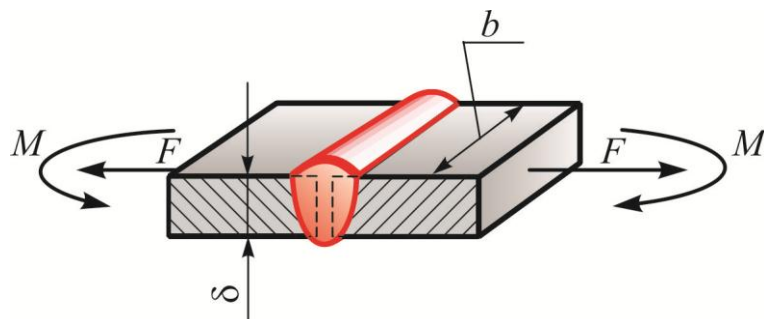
Схема нагружения сварного стыкового соединения растягивающей силой и изгибающим моментом
